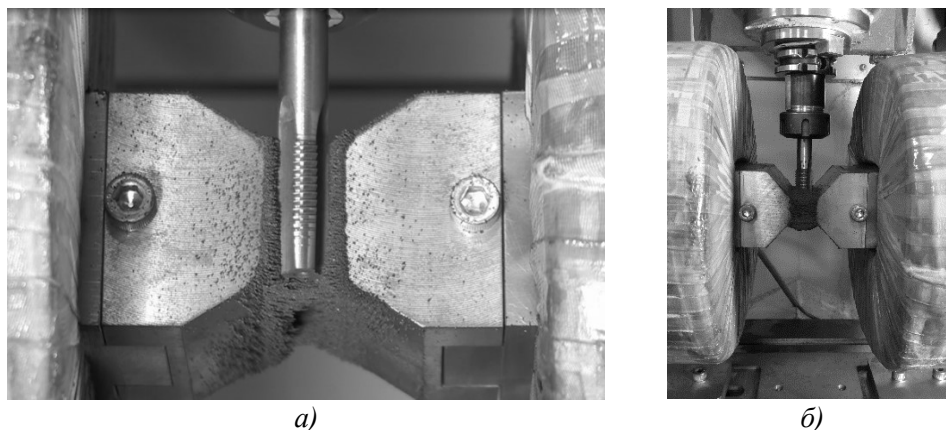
Магнитно-абразивная обработка метчика (а) и устройство (б)
